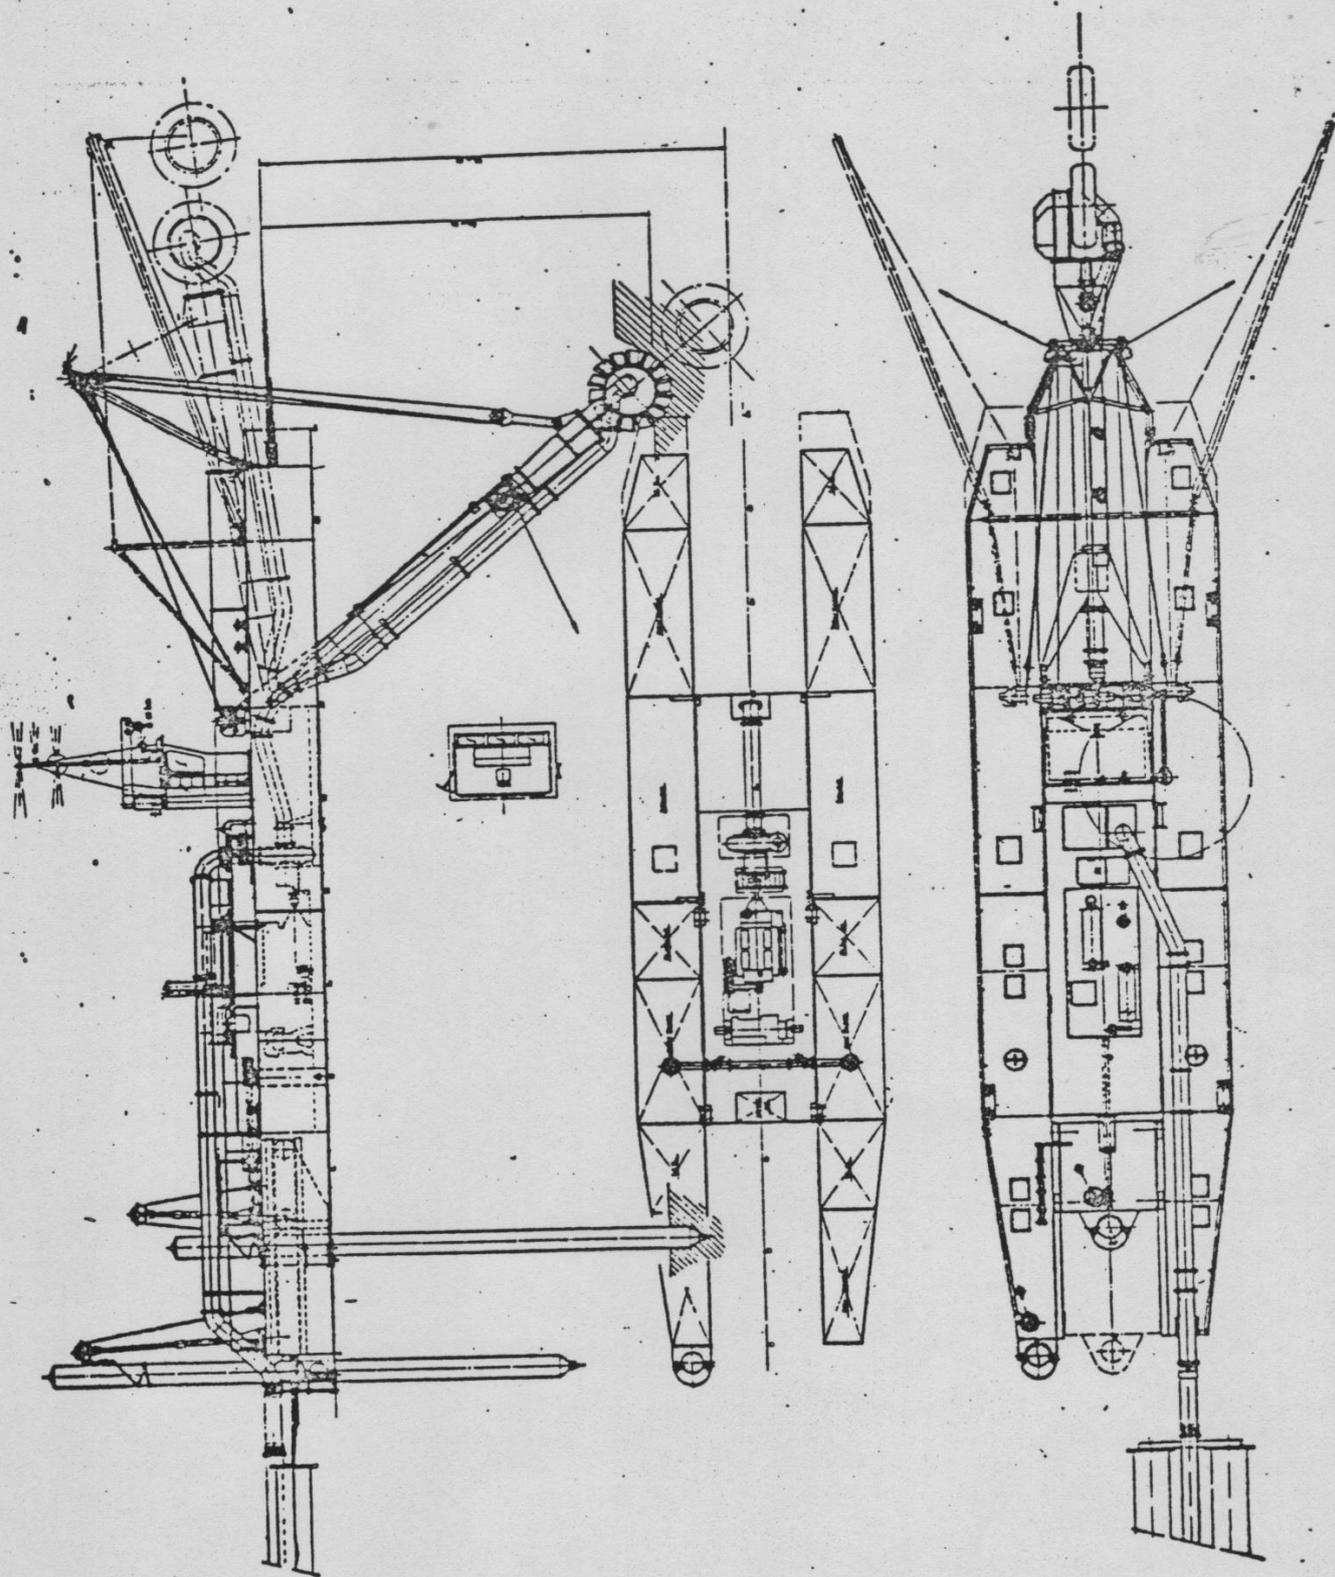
PLANTA GERAL DA DRAGA IHC BEAVERWHEEL 750
